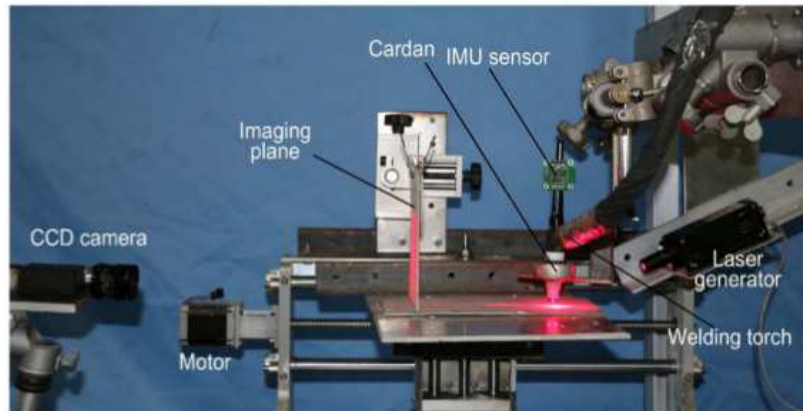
Sistema experimental de la soldadora[4].
